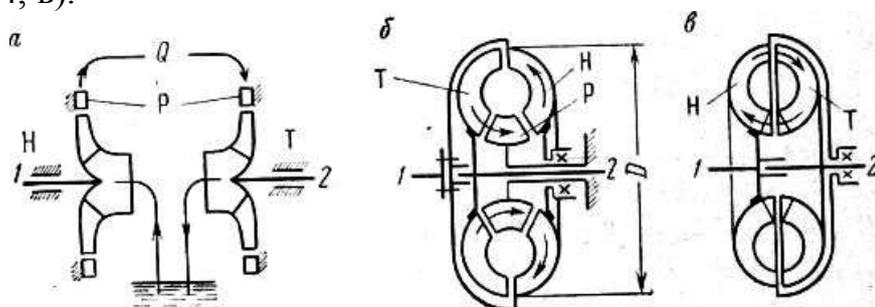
Схемы гидродинамических передач: а - насос и турбина; б - гидротрансформатор; в - гидромuфта; Н - насосное колесо; Т - турбинное колесо; Р - реактор; 1 - вал входного звена; 2 - вал выходного звена; D — активный диаметр
